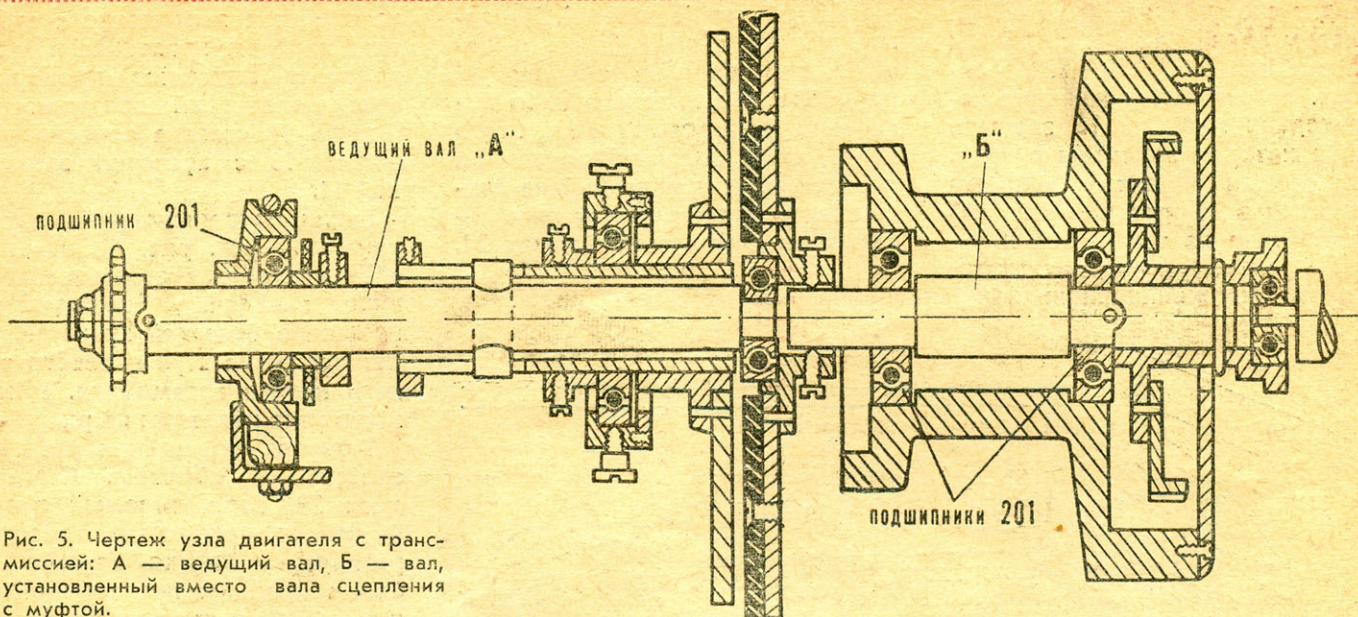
Чертеж узла двигателя с трансмиссией: А — ведущий вал, Б — вал, установленный вместо вала сцепления с муфтой.
